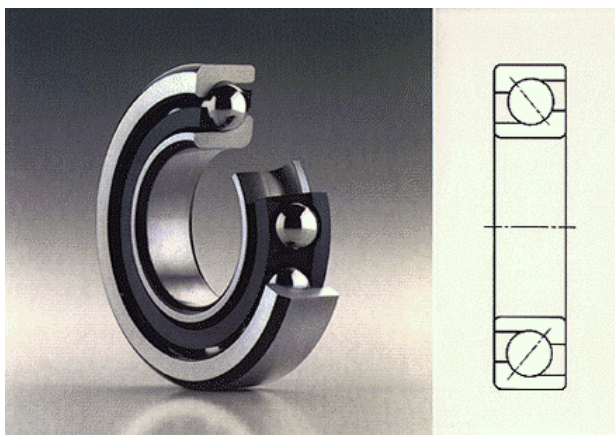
Rodamiento de bolas de contacto angular de una sola hilera
